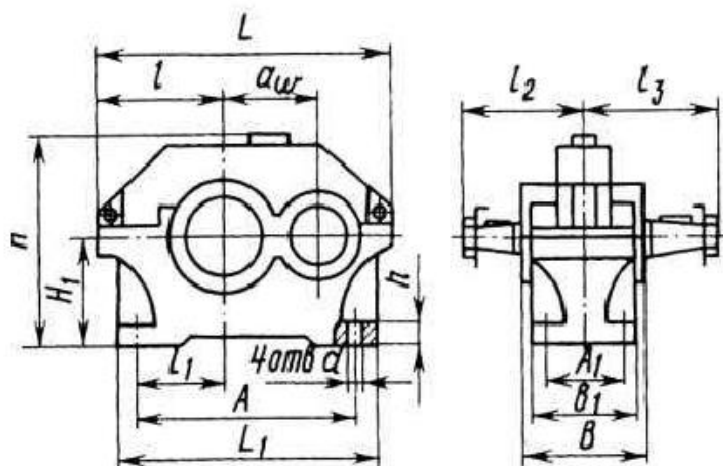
Схема сборки цилиндрического одноступенчатого редуктора (ГОСТ 20373-94)
